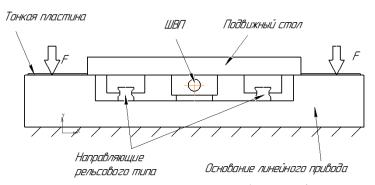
Конструкция вибродемпфера линейного привода в поперечном разрезе
